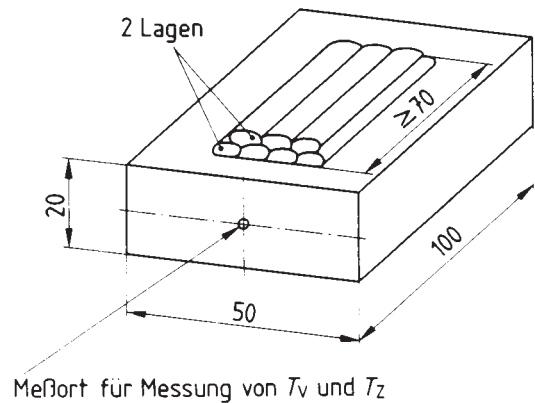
Prüfstück für das Gasschweißen (4-A1)
